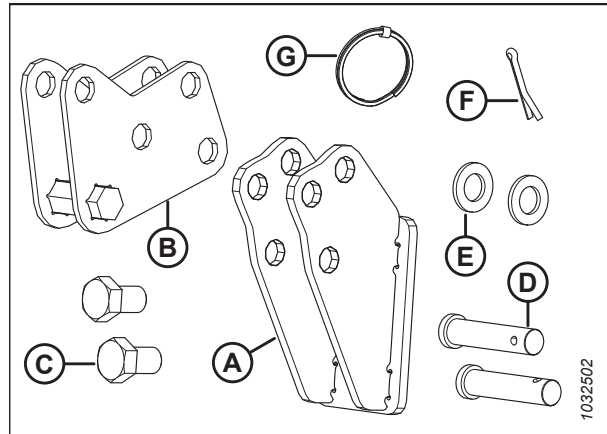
Sac de pièces pour le support avant-arrière MD N° 347580
